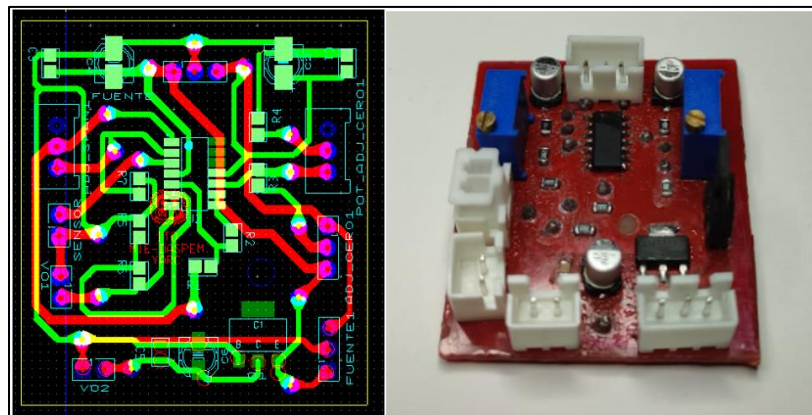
Diseño y manufactura de circuito escalador de voltaje.
